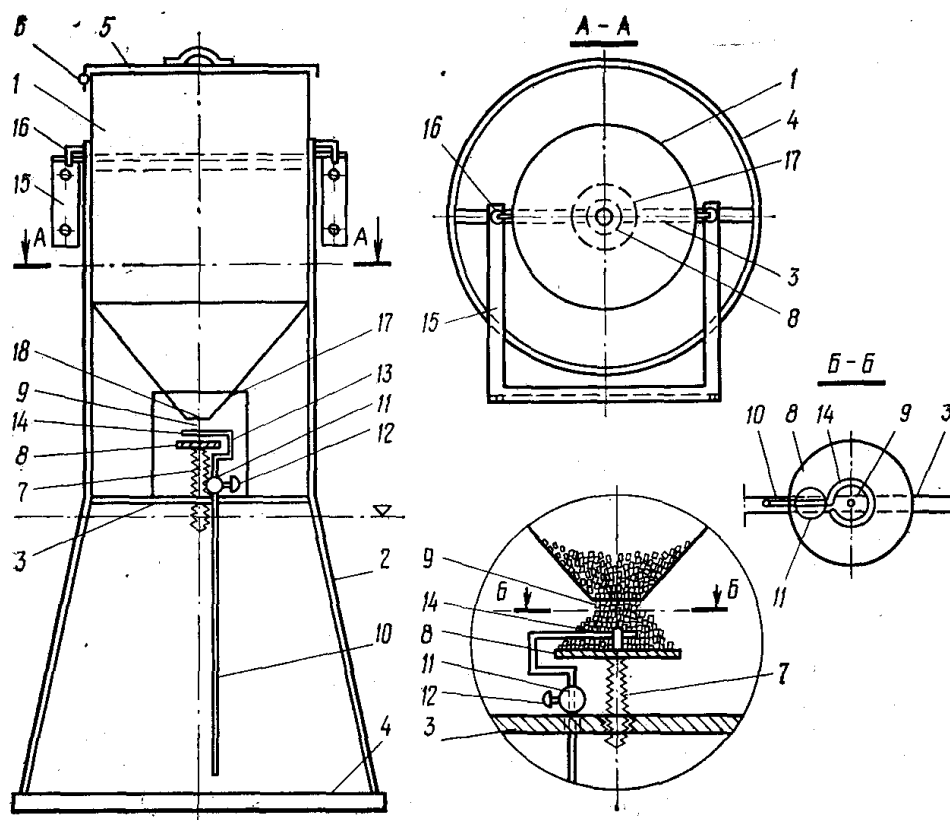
Автокормушка «Рефлекс»: 1 – бункер; 2 – стойка поддона; 3 – поперечная планка; 4 – поддон; 5 – крышка бункера; 6 – петля крышки; 7 – стойка с винтовой нарезкой; 8 – диск; 9 – штырь; 10 – маятник; 11 – шаровая опора; 12 – стопорный винт; 13 – изгиб маятника; 14 – кольцевой сбрасыватель; 15 – кронштейн; 16 – крючья; 17 – защитный кожух
